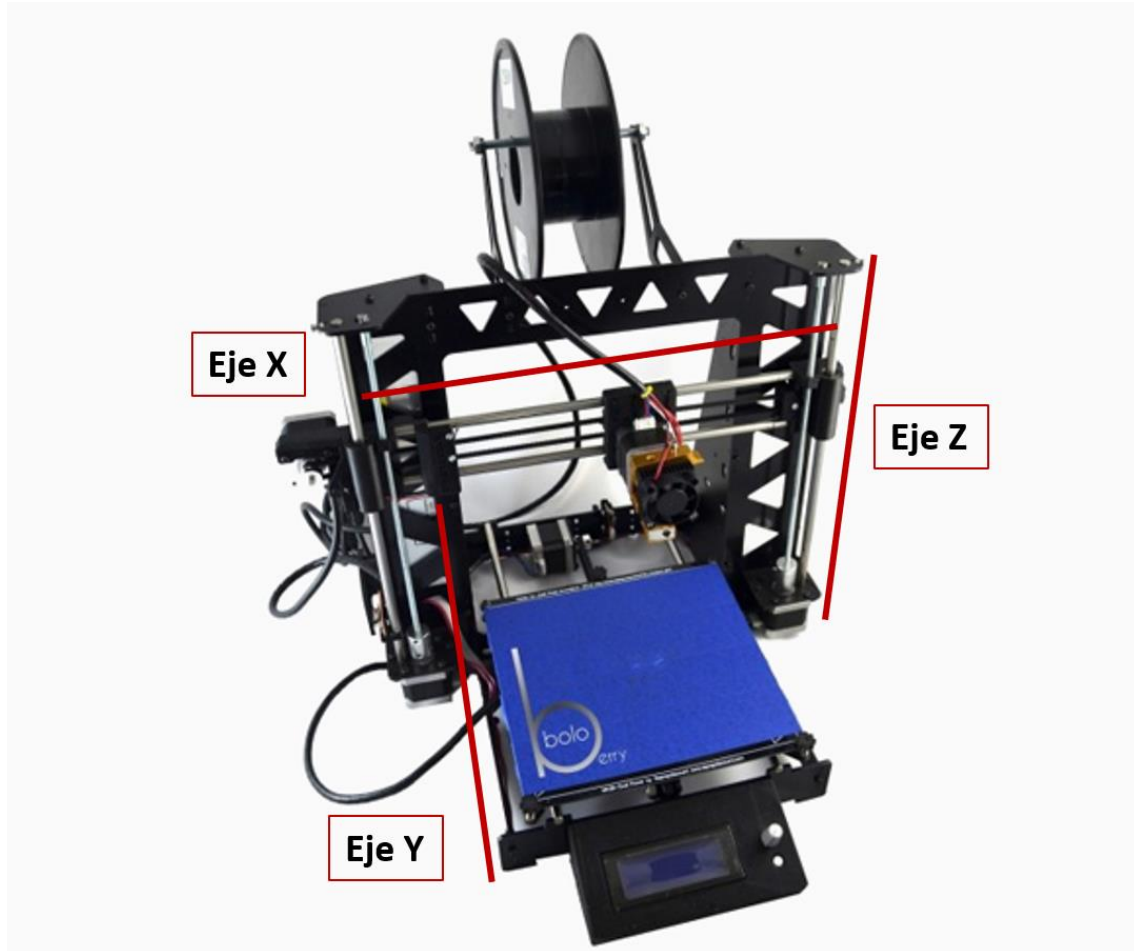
kit Prusa i3 Steel Pro de Boloberry con marco tipo pórtico de aluminio. Fuente: Boloberry
